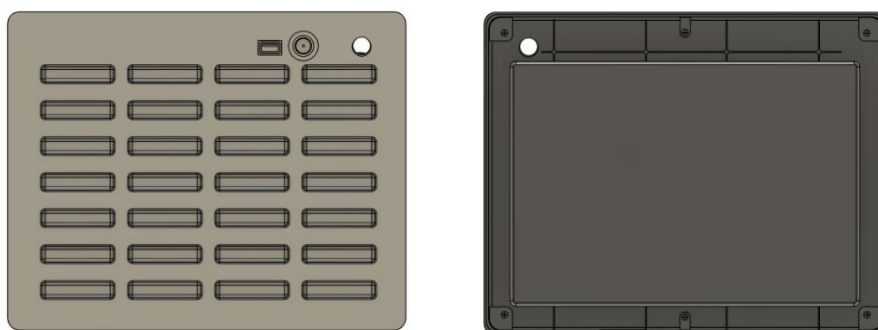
Лицевая и внутренняя часть верхней части корпуса
